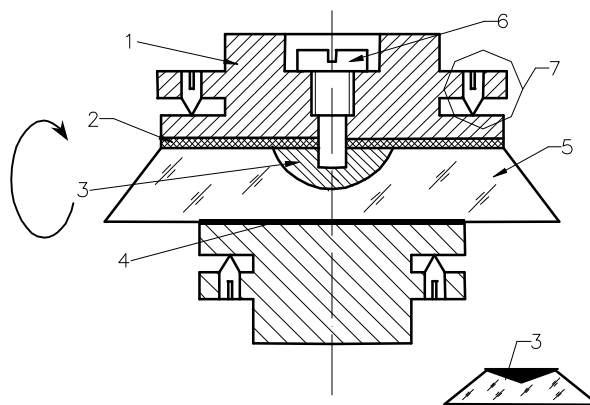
Кріплення призми $AP-0^0$ (конструкція повинна обертатися): 1 – корпус (оправа); 2 – еластична прокладка; 3 – шпонка; 4 – прокладка; 5 – призма; 6 – кріпильний гвинт; 7 – пружинне кріплення призми
